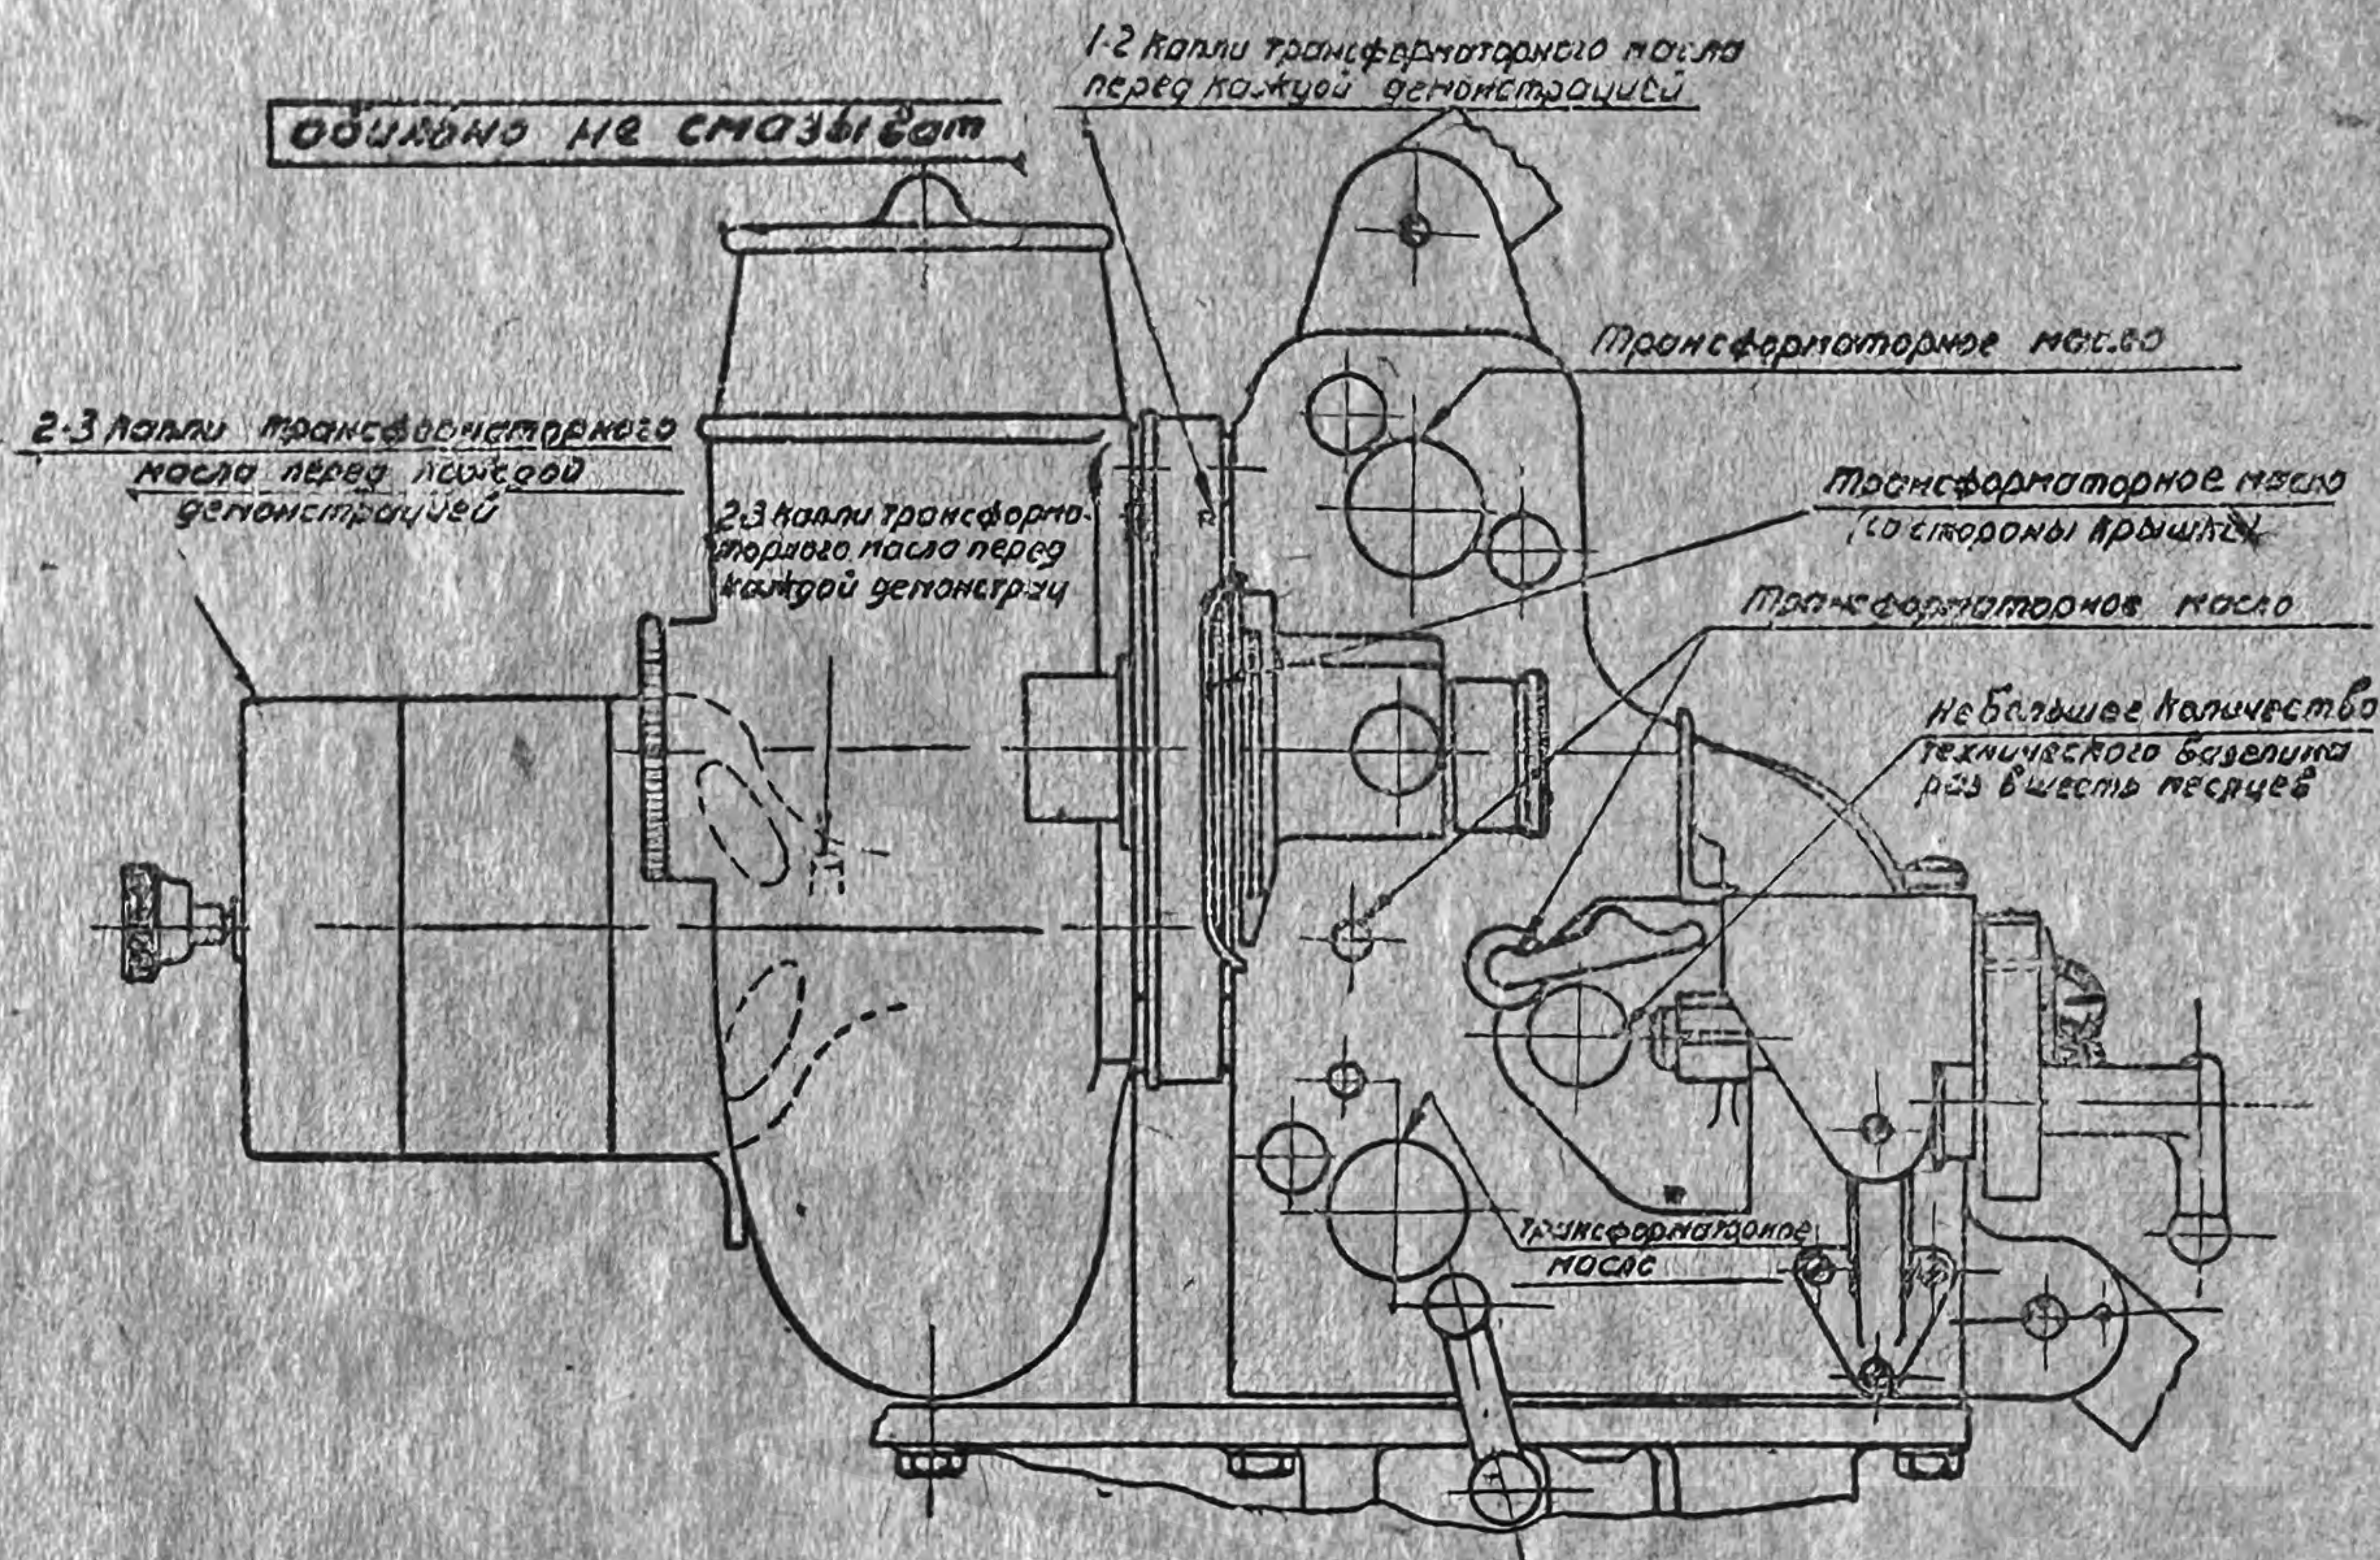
Схема смазки механизма кинопроектора 16-3СП-5.
